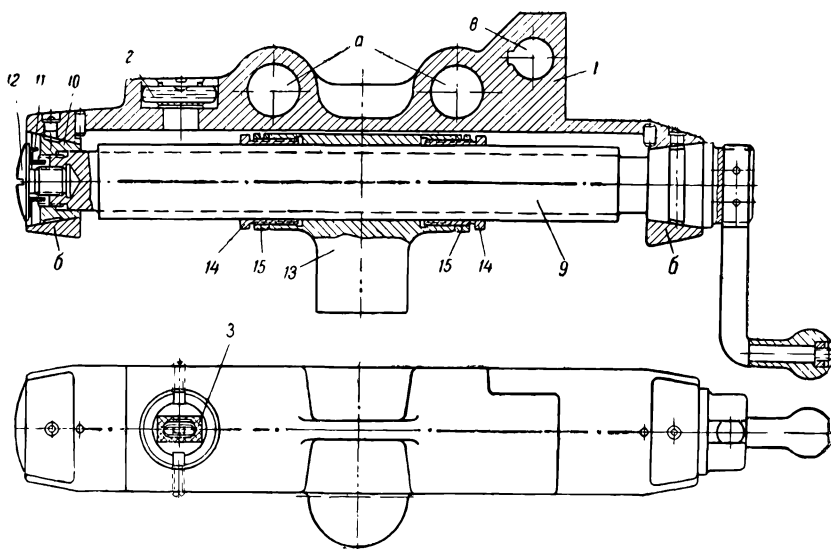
Вертлюг 120-мм миномёта обр. 1938 г. с поворотным механизмом; 1 — вертлюг; 2 — уровень; 3 — штorka уровня; 4 — винт поворотного механизма; 5 — конус; 6 — шайба; 7 — пробка; 8 — матка поворотного механизма; 9 — регулирующие гайки; 10 — контргайки; 11 — матка поворотного механизма; 12 — регулирующие гайки; 13 — контргайки; 14 — отверстие для крепления штоков амортизатора; 15 — проушины для винта поворотного механизма; 16 — отверстие под переходный кровштейн
